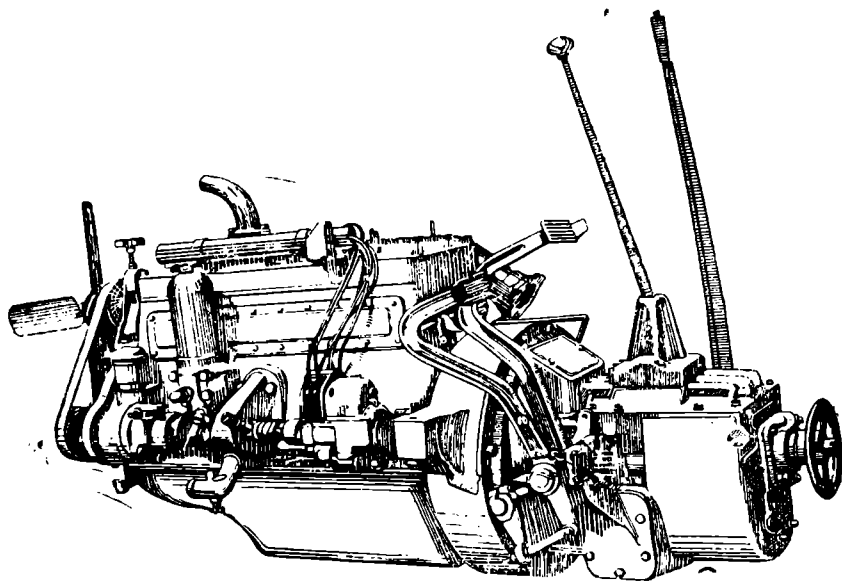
Двигатель ЗИС-21 (вид со стороны магнето).
